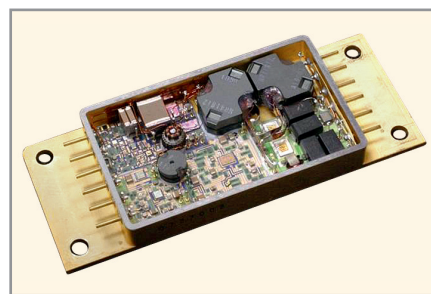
Преобразователь серии НТА в корпусе 102 × 38 × 11 мм со снятой верхней крышкой
